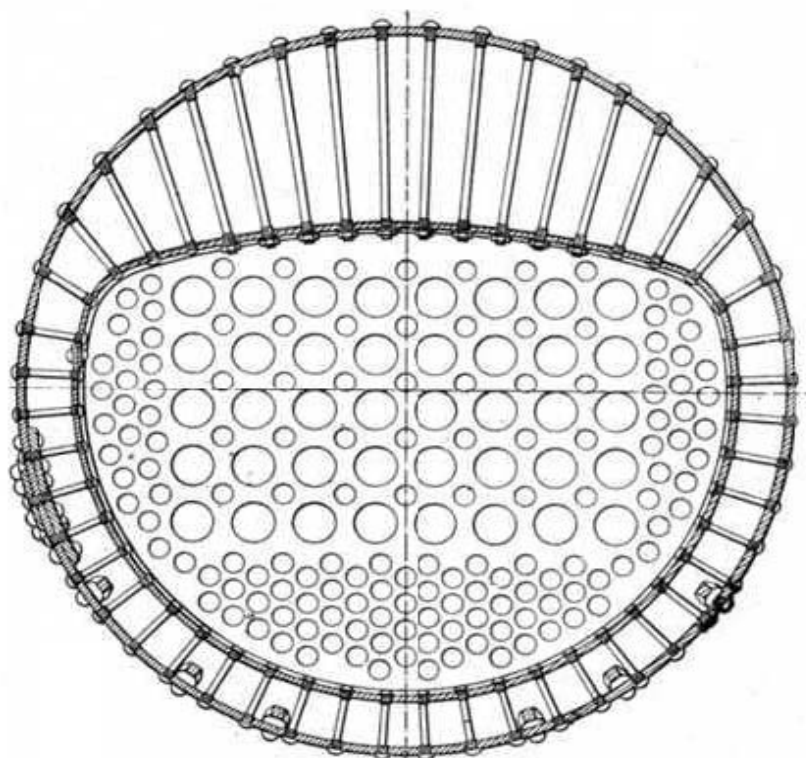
Hogar de cobre de las locomotoras Mountain del P.L.M. Corte transversal por la cámara de combustión
